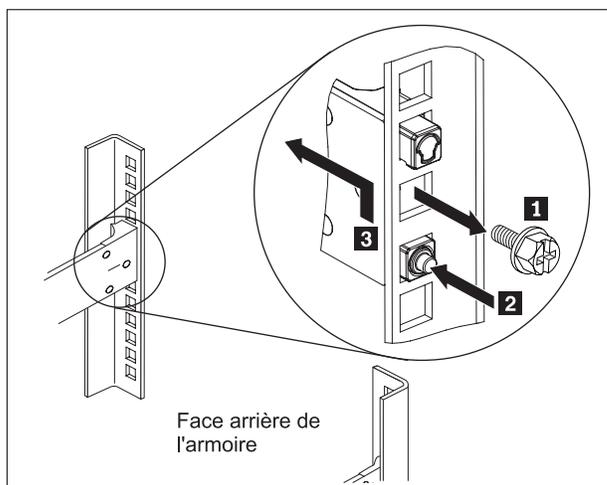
Levage de l'arrière du dispositif pour la dégager de la glissière
